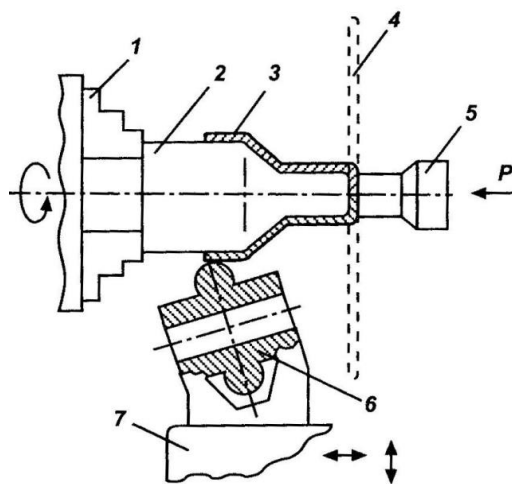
Ротаційне витягування заготовки на токарному верстаті:
